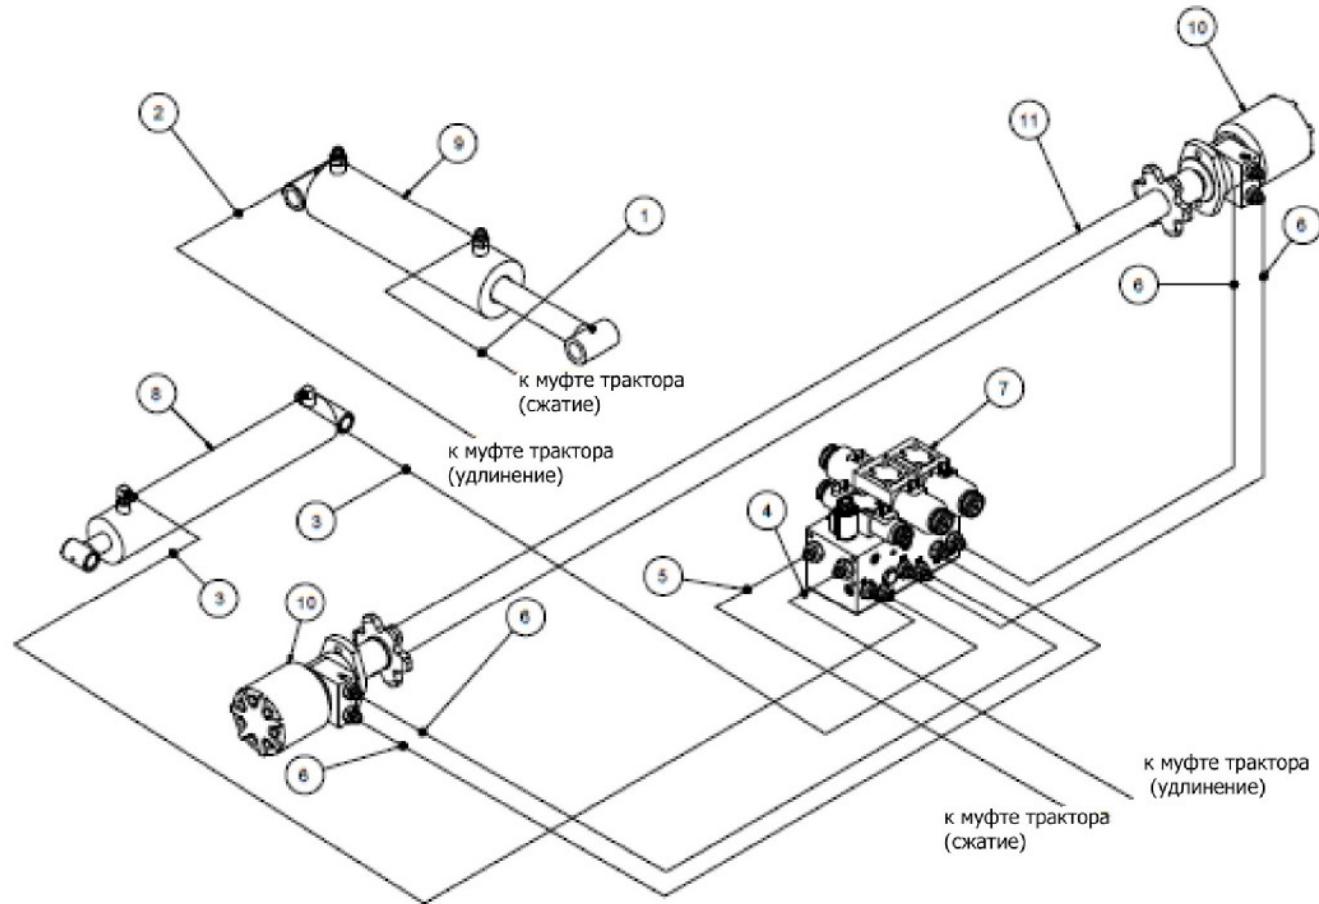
Чертеж сборки гидравлики тележки – 815602
